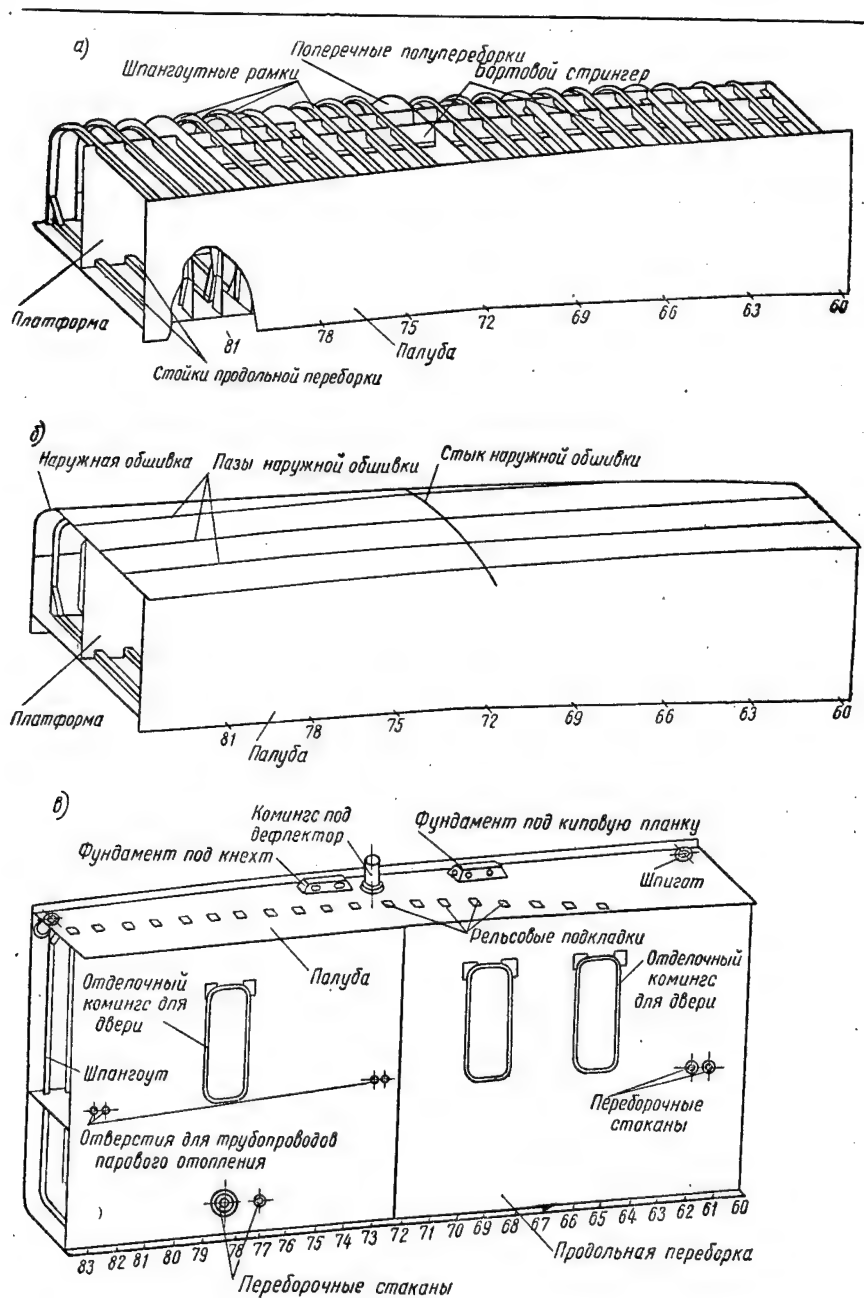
Последовательность сборки и сварки бортовой секции без постели
